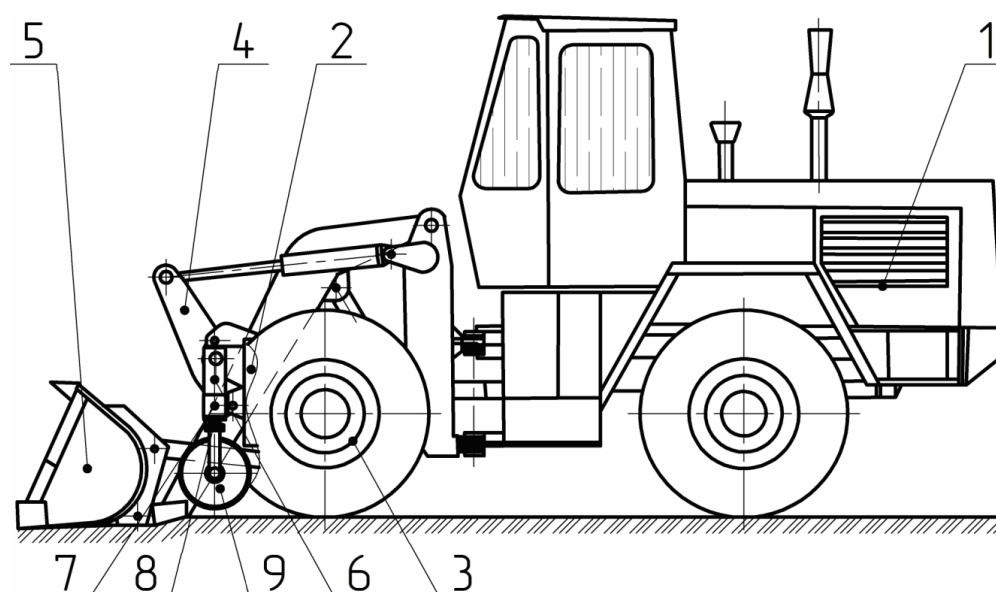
Конструкция устройства для выравнивания вертикальных нагрузок на мосты фронтального погрузчика
